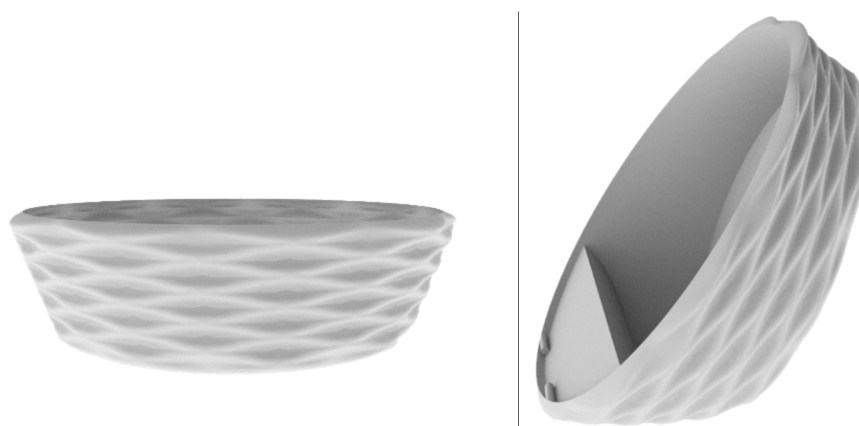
Формообразование корпуса. Слева геометрическая форма, взятая за основу, справа корпус ангара.
